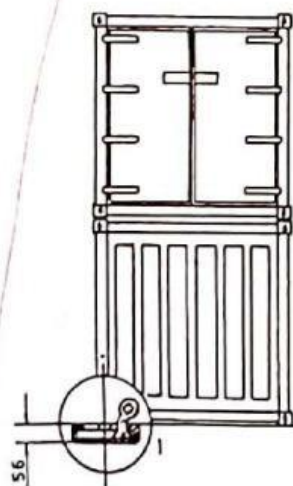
Fundamento de trinca para pie de elefante.
